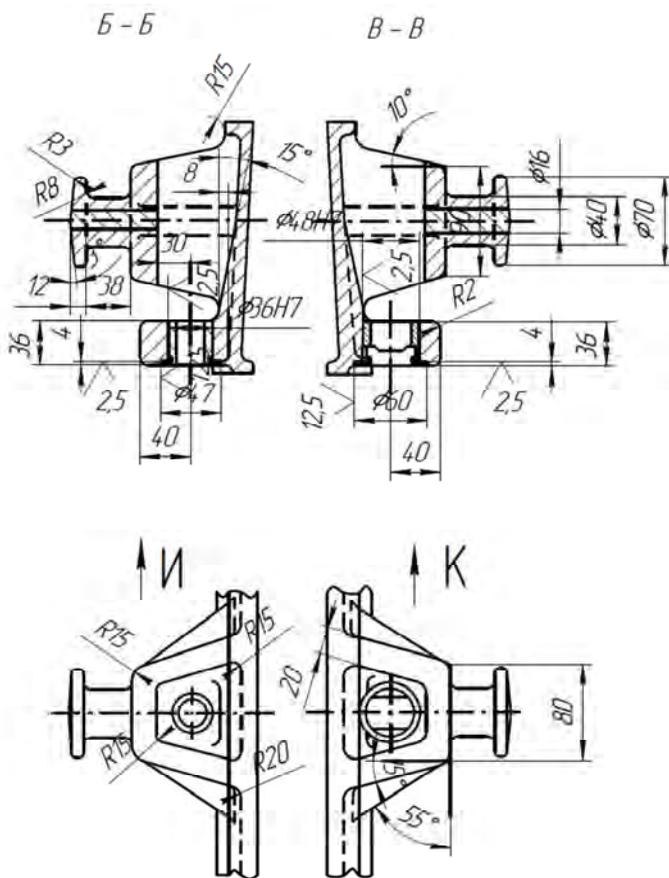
Конструкция корпуса с цапфами для комбинированных опок высотой 200 мм
